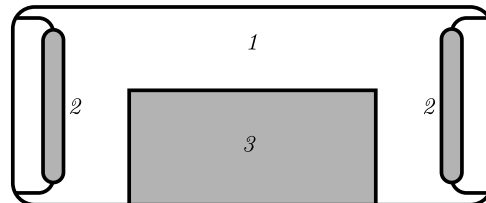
Схема плавильной печи с косвенным нагревом: 1 — камера, 2 — нагреватели, 3 — обрабатываемый материал.
